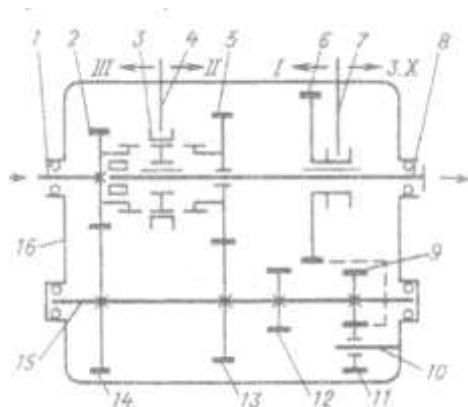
Схема тривальної триступінчастої коробки передач: 1 - ведучий вал; 2 - шестерня ведучого вала; 3 - зубчаста муфта; 4 і 7 - вилки включення відповідно другої, третьої та першої передач і заднього ходу; 5 - шестерня другої передачі; 6 - шестерня першої передачі і заднього ходу; 8 - ведений вал; 9 - проміжна шестерня заднього ходу; 10 - вісь; 11 шестерня включення заднього ходу; 12 і 13 - ведучі шестерні відповідно першої та другої передач; 14 - шестерня проміжного вала; 15 - проміжний вал; 16 - корпус коробки передач
